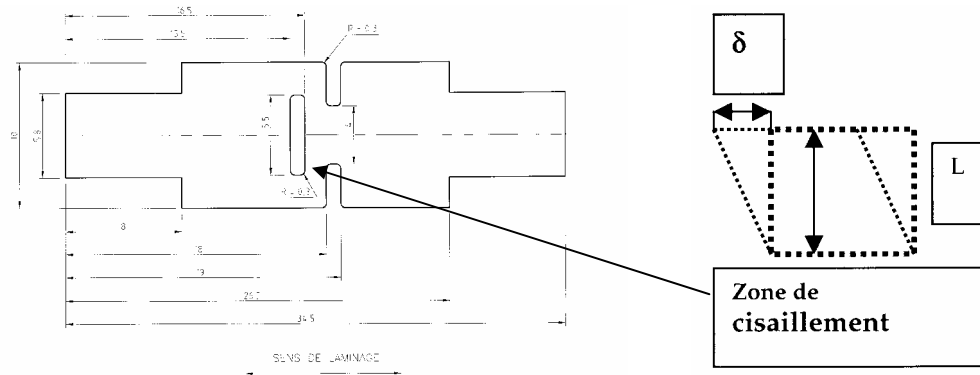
Géométrie de l'éprouvette de cisaillement.
